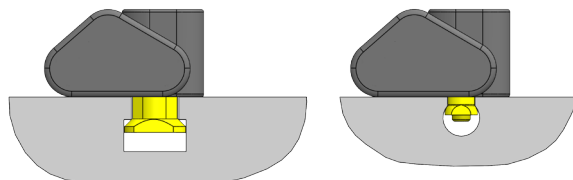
Пазовые сухари зафиксированы в пазу (вид сбоку; Т-образный паз на рис. слева, С-образный паз справа)
